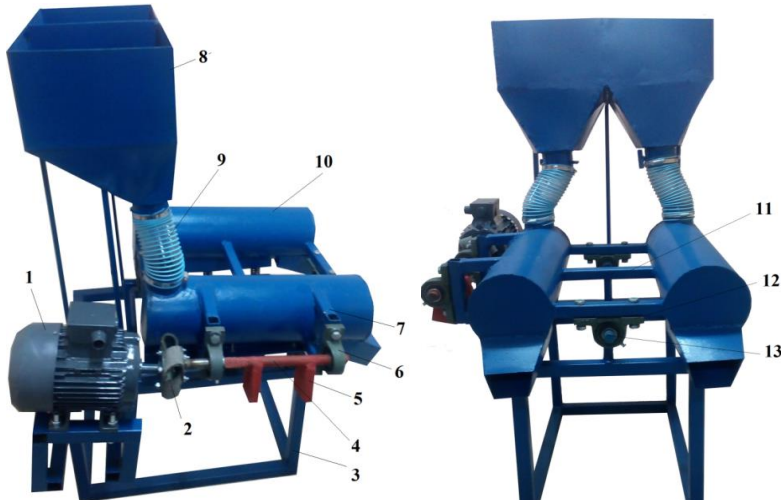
Конструкція вібраційного млина кутових коливань : 1 – електродвигун; 2 – еластична муфта; 3 – станина; 4 – приводний вал; 5 – дебаланси; 6 – підшипникові вузли віброприводу; 7 – стійки; 8 – завантажувальний бункер; 9 – живильні патрубки; 10 – помольні камери; 11 – траверси; 12 – підшипниковий вузол центральної вісі; 13 – вісь.
